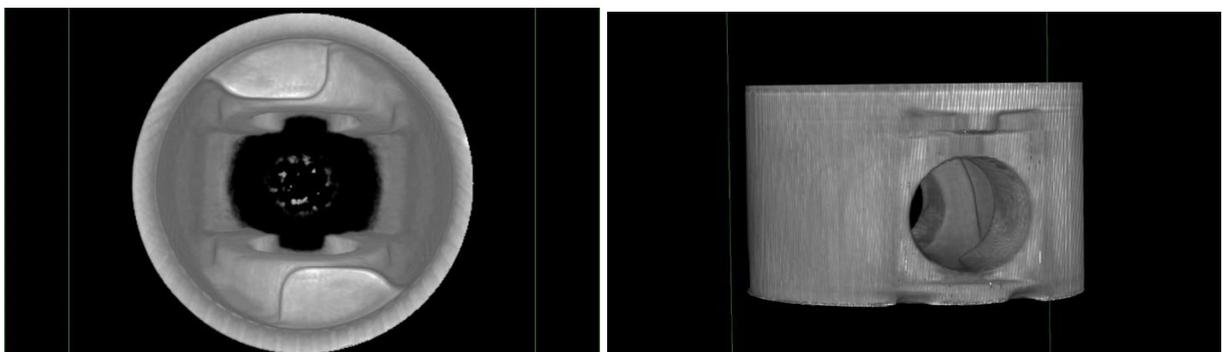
Перспективные виды изображения поршня, слева – торцевой вид поршня, справа – фронтальный вид
